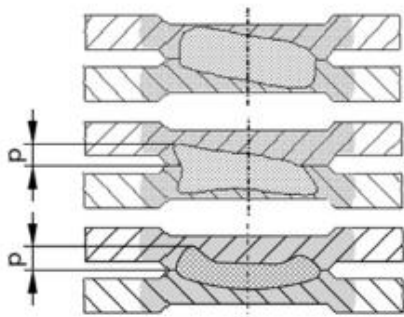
Representação de assimetria no ponto de soldadura
